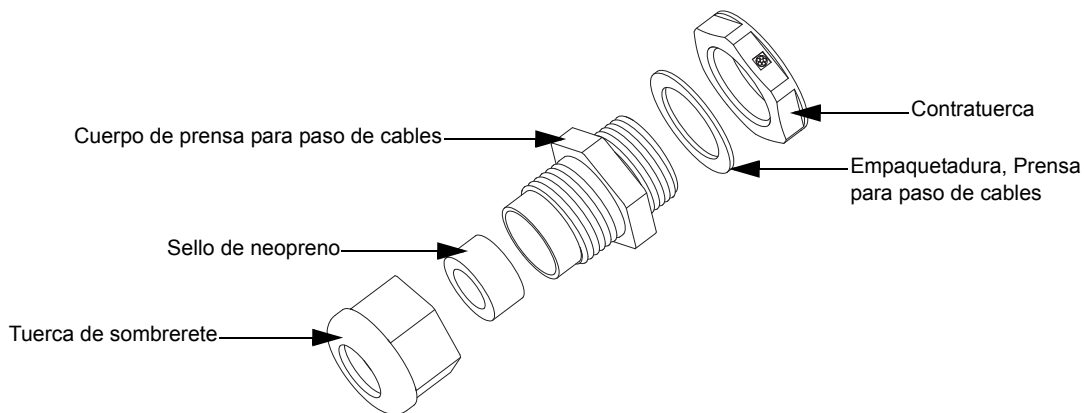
Montaje de prensa para paso de cables con empaquetadura
